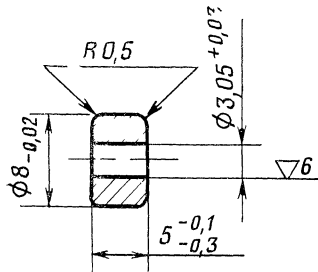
Ось рычага шептала 7-10. Ось спускового рычага 7-17
